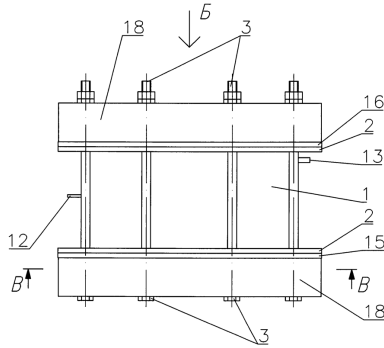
Взрывная камера, вид Б, сечение В-В [6], где: 1 – металлический наружный корпус в форме цилиндра; 2 и 3 – верхние и нижние упорные кольца; 13 – штуцер; 15 – дно; 16- крышка; 18 – металлические кольца.
